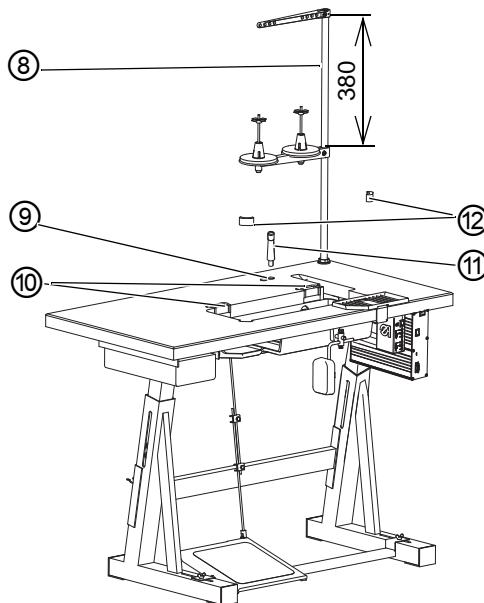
Kompletace desky podstavce 1 - dlouhé stroje
